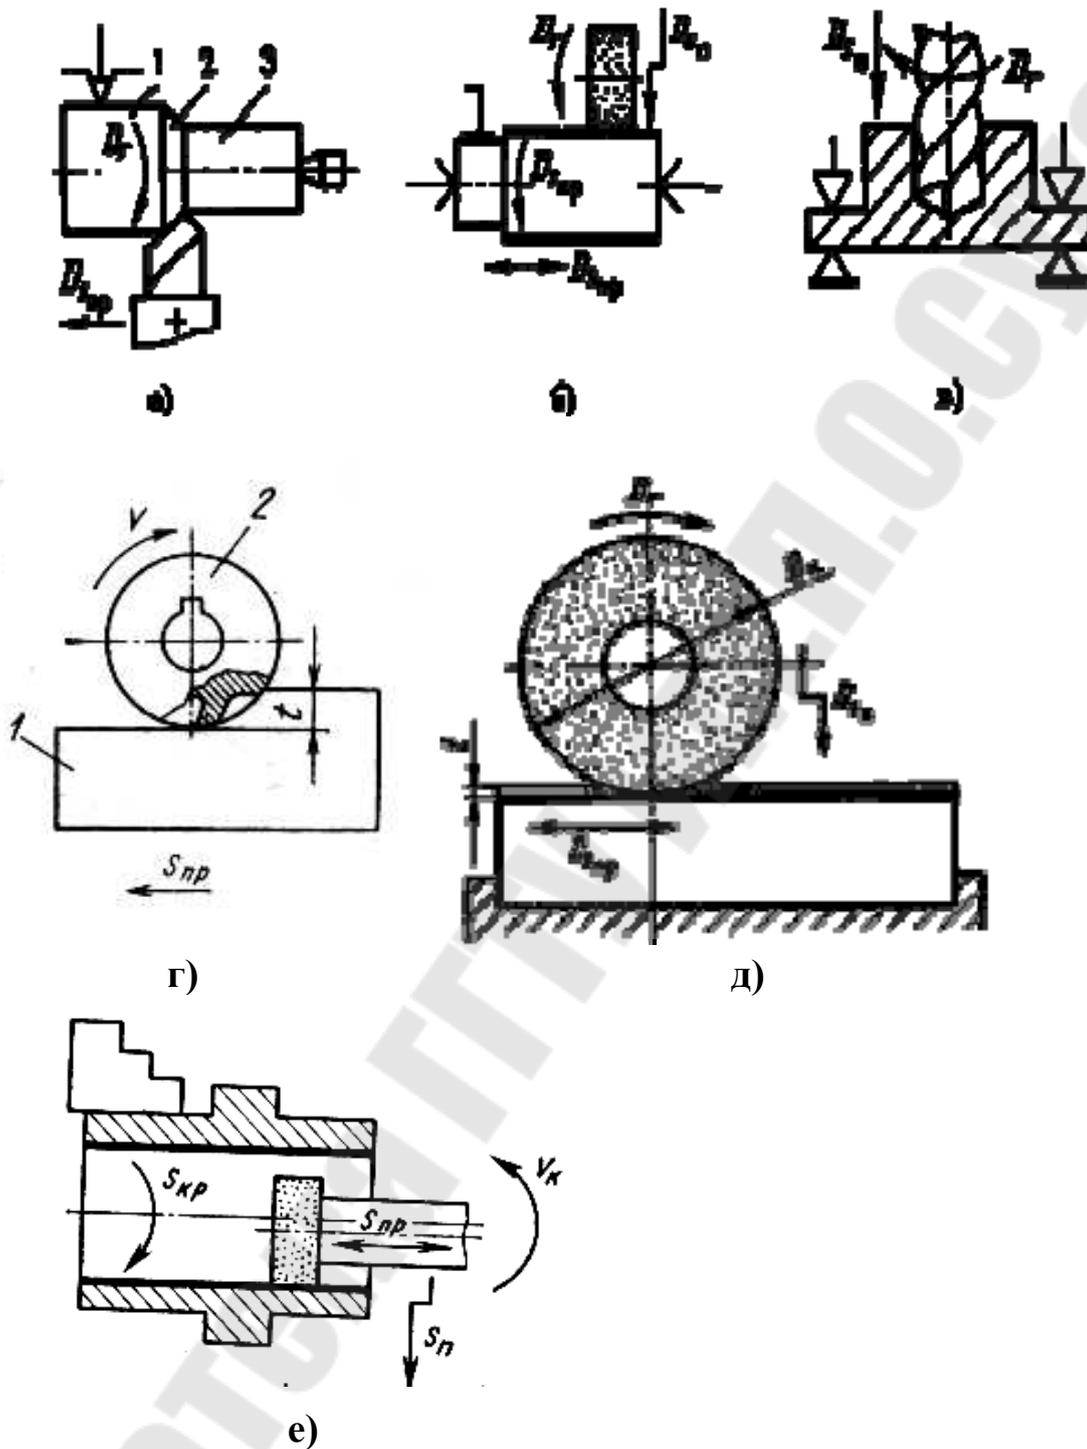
Схемы обработки заготовок: а – точением; б – шлифованием на круглошлифовальном станке; в – сверлением; г – фрезерованием; д – плоским шлифованием; е – внутренним шлифованием.
